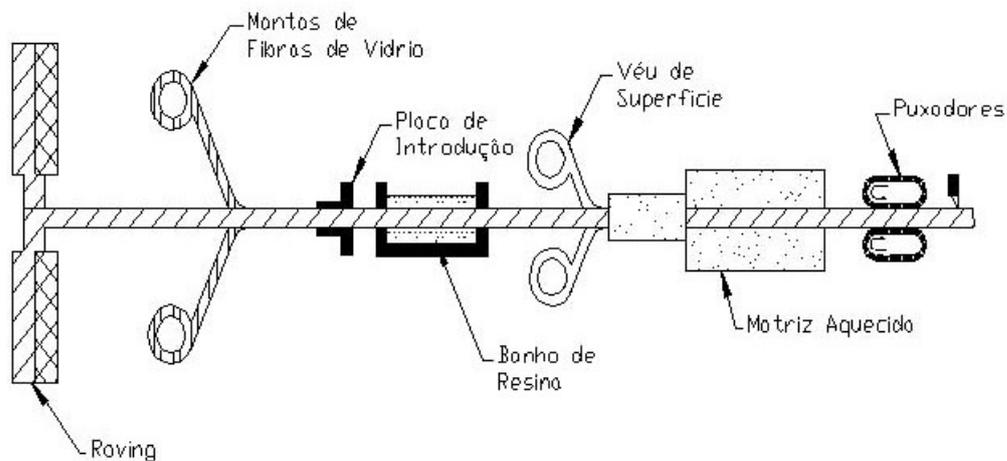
Componentes básicos da máquina de pultrusão. Retirado www.wpp.com.br (2005)
